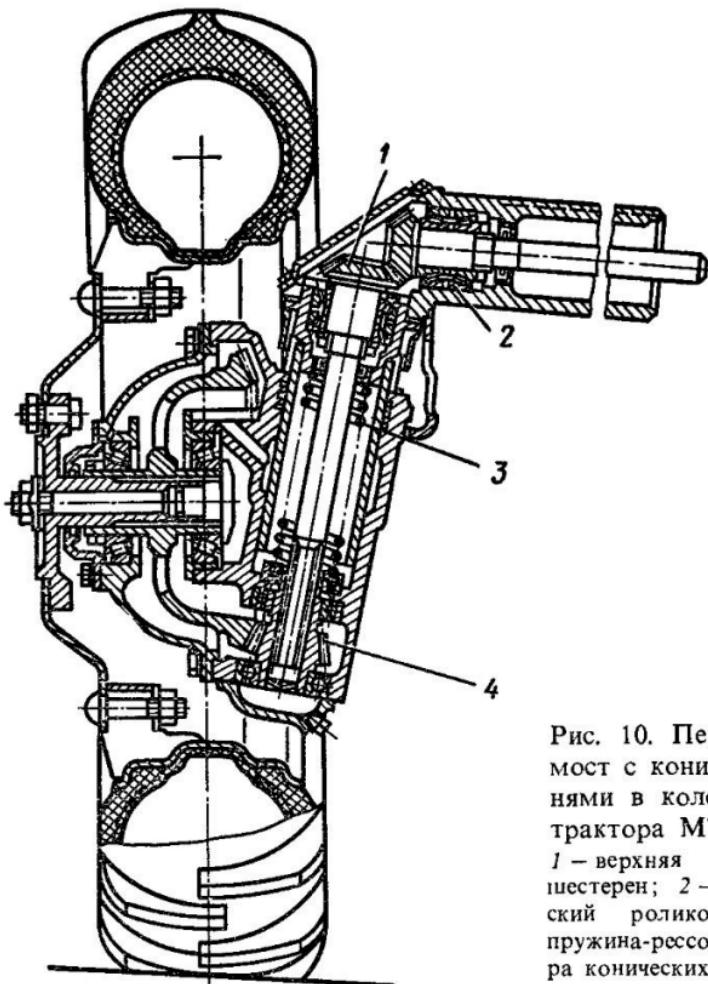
Передний ведущий мост с коническими шестернями в колесном редукторе трактора МТЗ-82:
